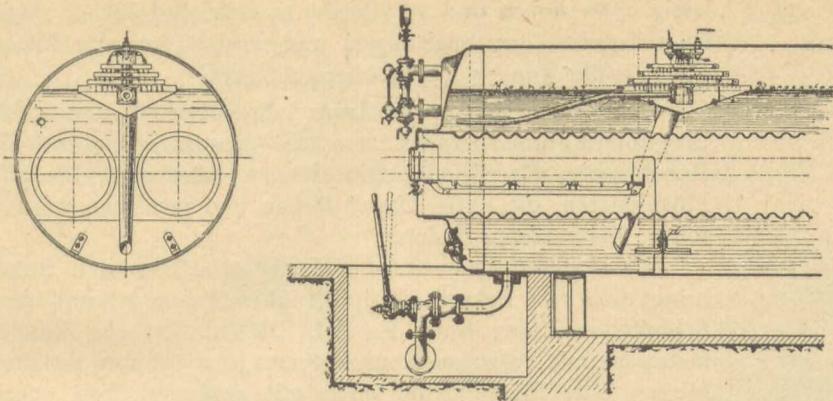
Kessel mit „Vapor“ Apparat und Abschlammventil „Vesuv“.
